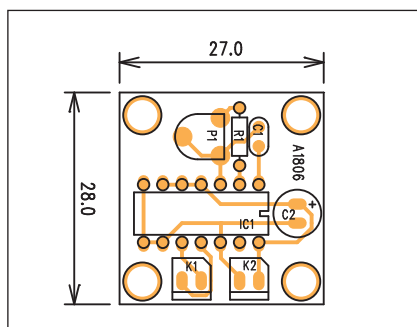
Obrazec desky spojů spořiče (strana BOTTOM)
